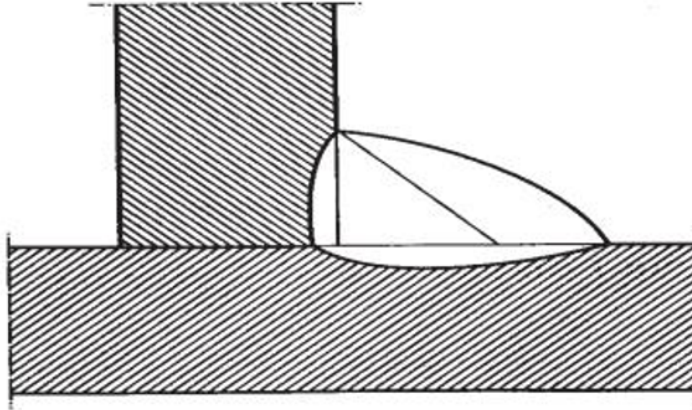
Эскиз дефекта сварного шва
